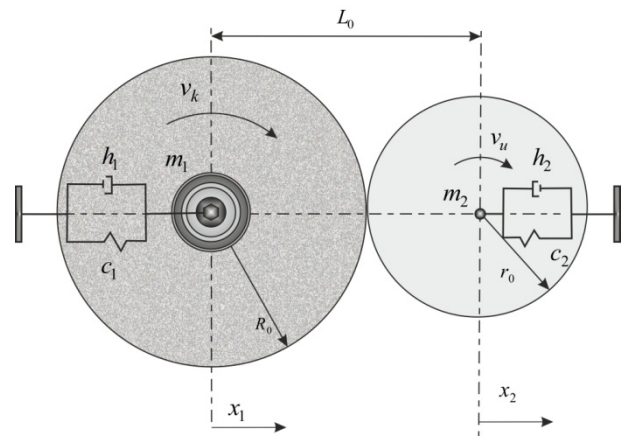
Эквивалентная схема динамической системы круглошлифовального станка
